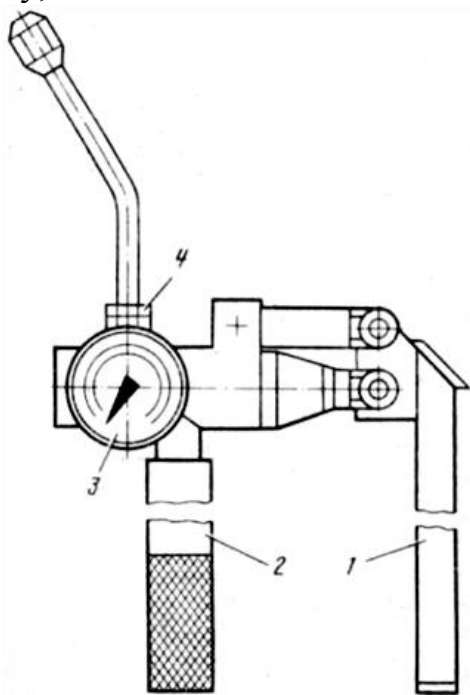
Приспособление КИ-16301А (механотестер) для проверки форсунок:
